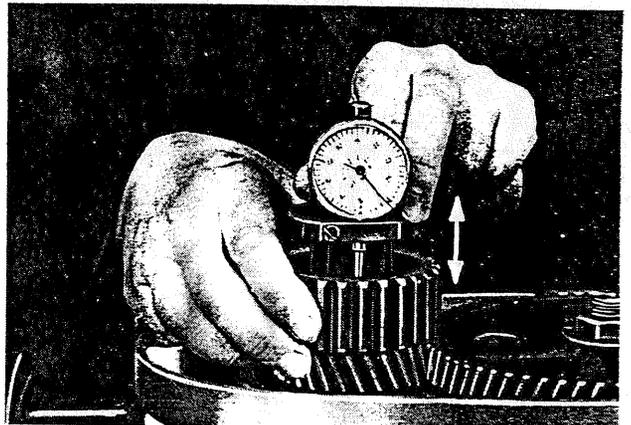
Mesurer le jeu axial du disque récepteur d'embrayage
